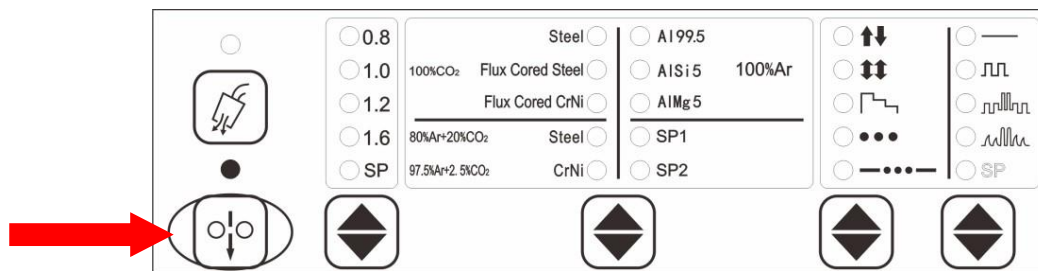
Кнопка "Проверка подачи проволоки" на панели управления сварочного источника питания
